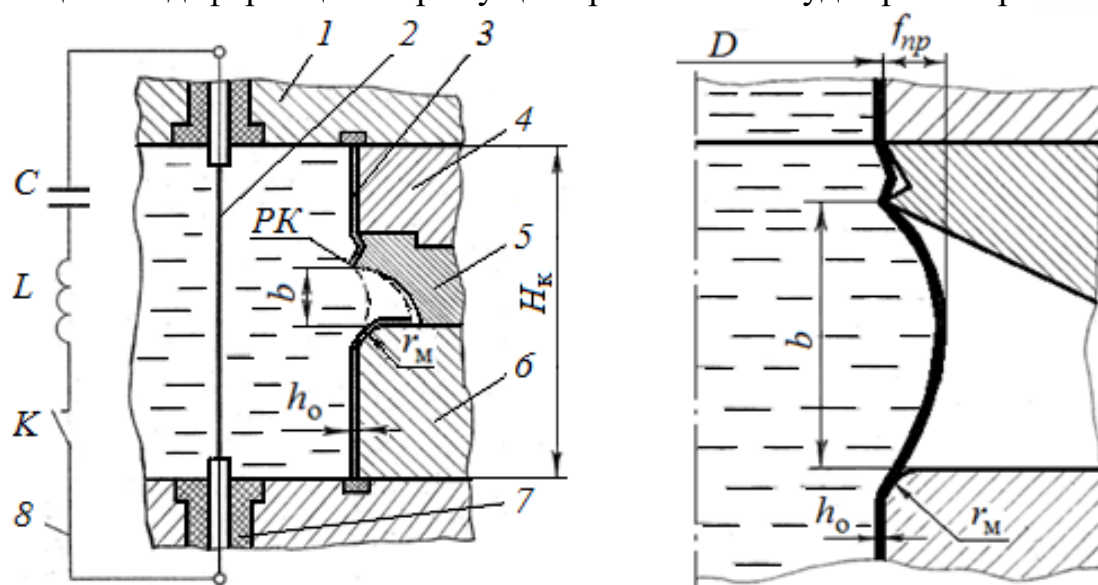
Технологическая схема процесса электрогидроимпульсной штамповки тонкостенной цилиндрической заготовки с осевым разрядом: а) формообразование фланца; б) момент обрезки заготовки на режущей кромке ножа.
